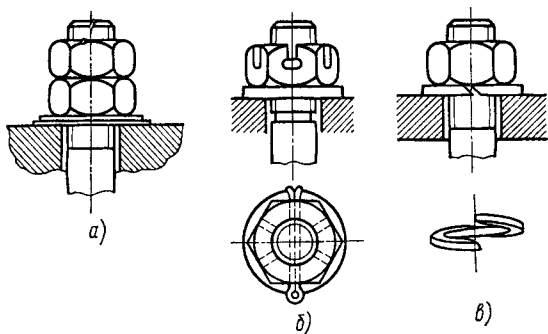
Замковые устройства резьбовых соединений (гаечные замки)
